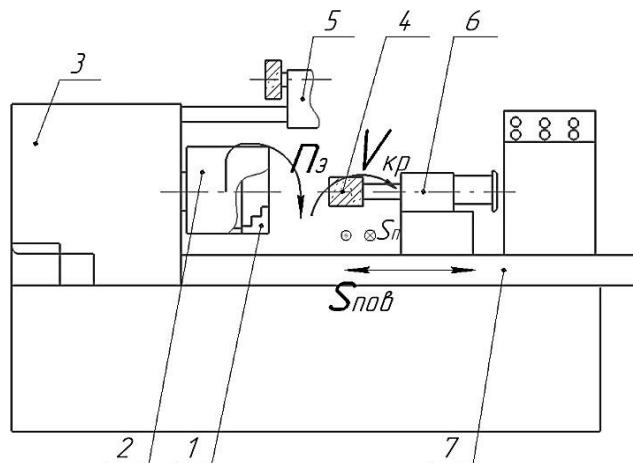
Схема універсального внутрішньошлифувального верстата
